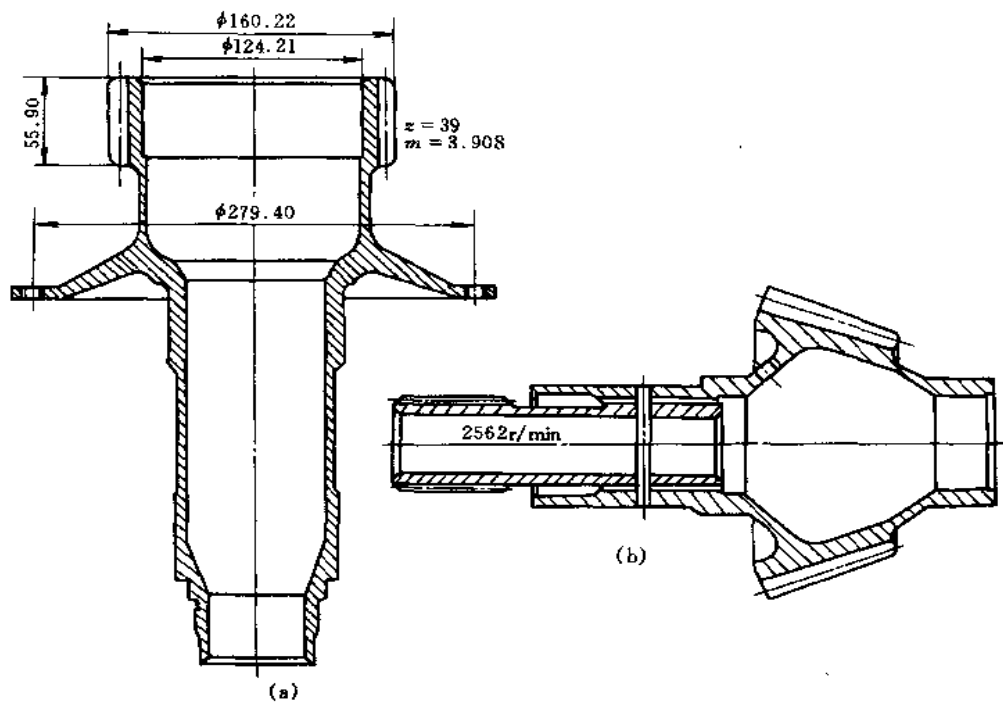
直升飞机的传动装置及空心齿轮轴 (c)
